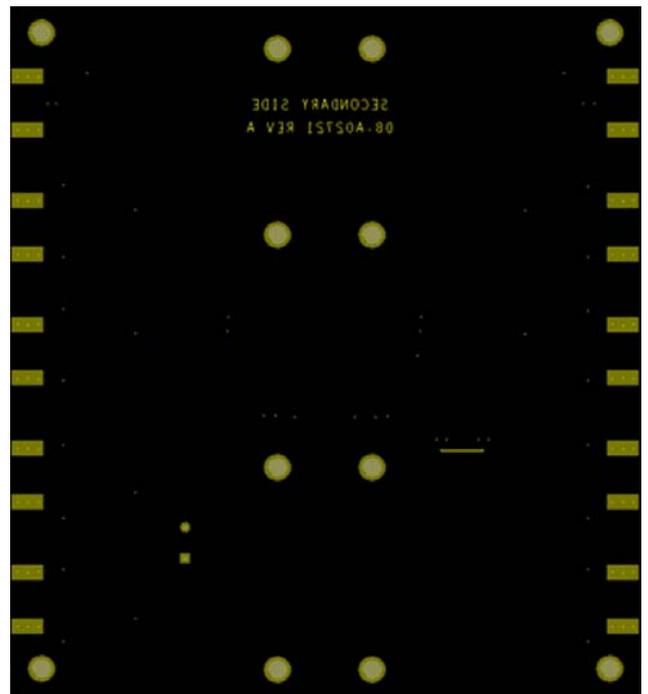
層低ノイズ PCB レイアウトの底面層 4
